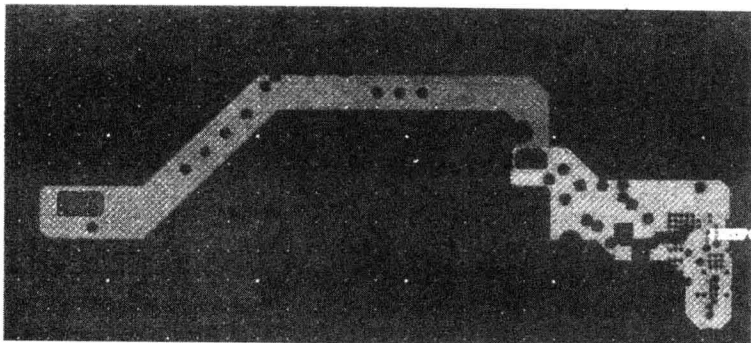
典型的电源传输线跨过封装以及 PCB 版图
